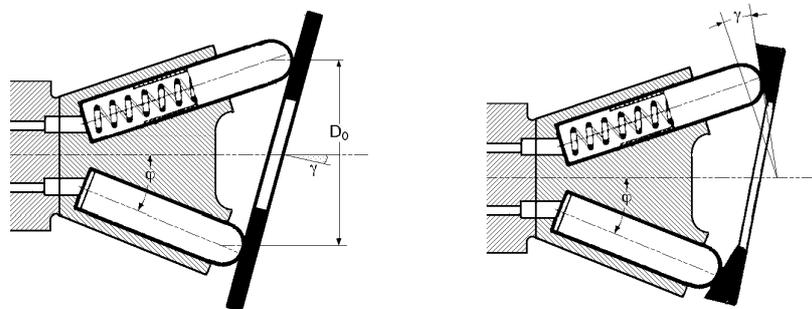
Compresores rotativos de émbolos inclinados, con disco cónico
